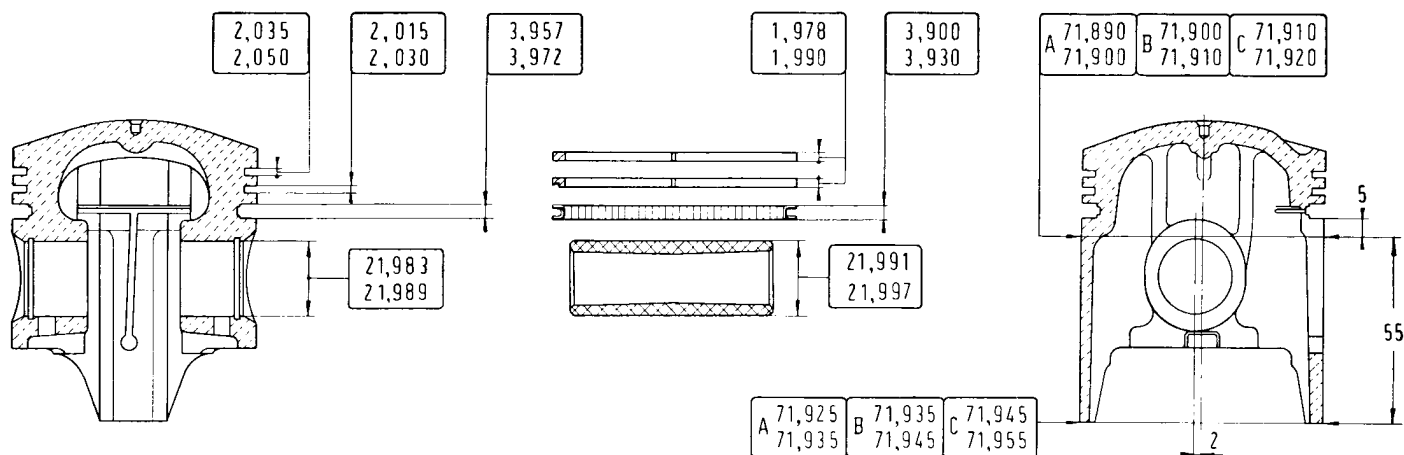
Dati principali dello stantuffo, del perno e degli anelli elastici, montati sul motore 116.000.
